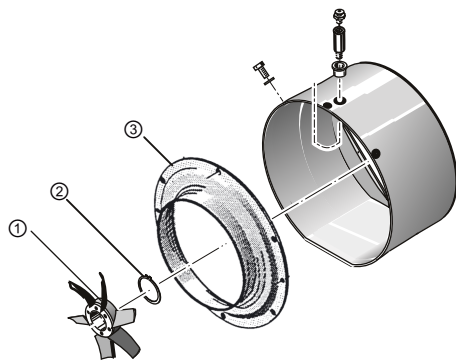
Вентиляция (принципиальная схема с осевым вентилятором)
